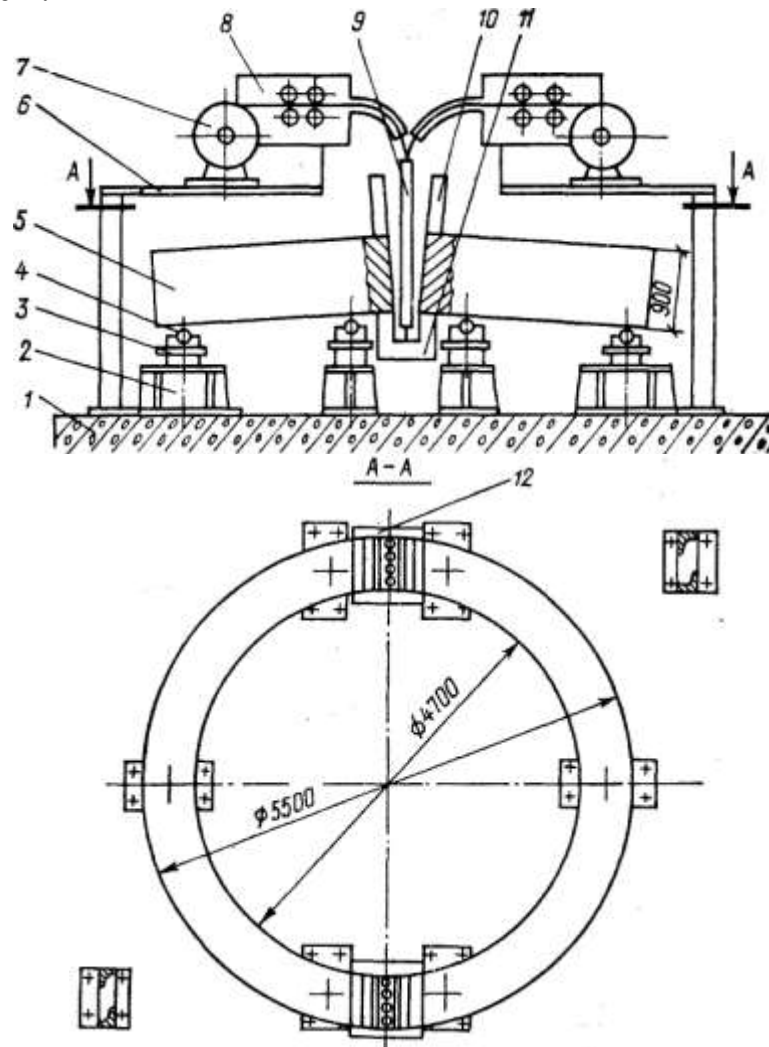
Электрошлаковая сварка бандажей цементных печей на монтажной площадке
